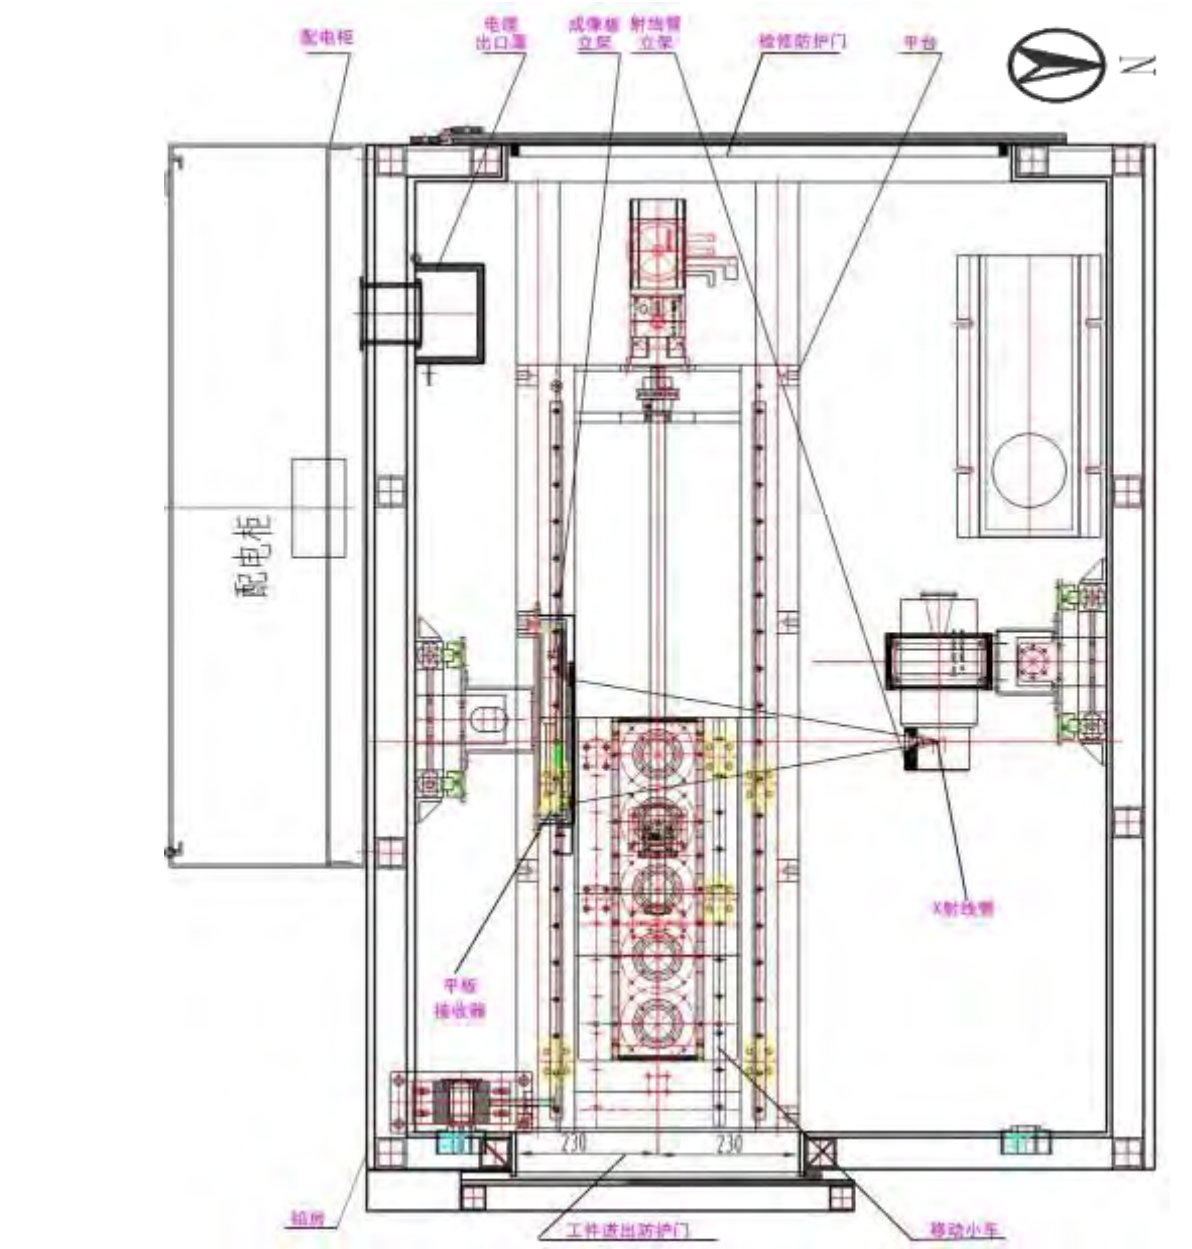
(a) X 射线实时成像检测系统自带铅房平面布置图
